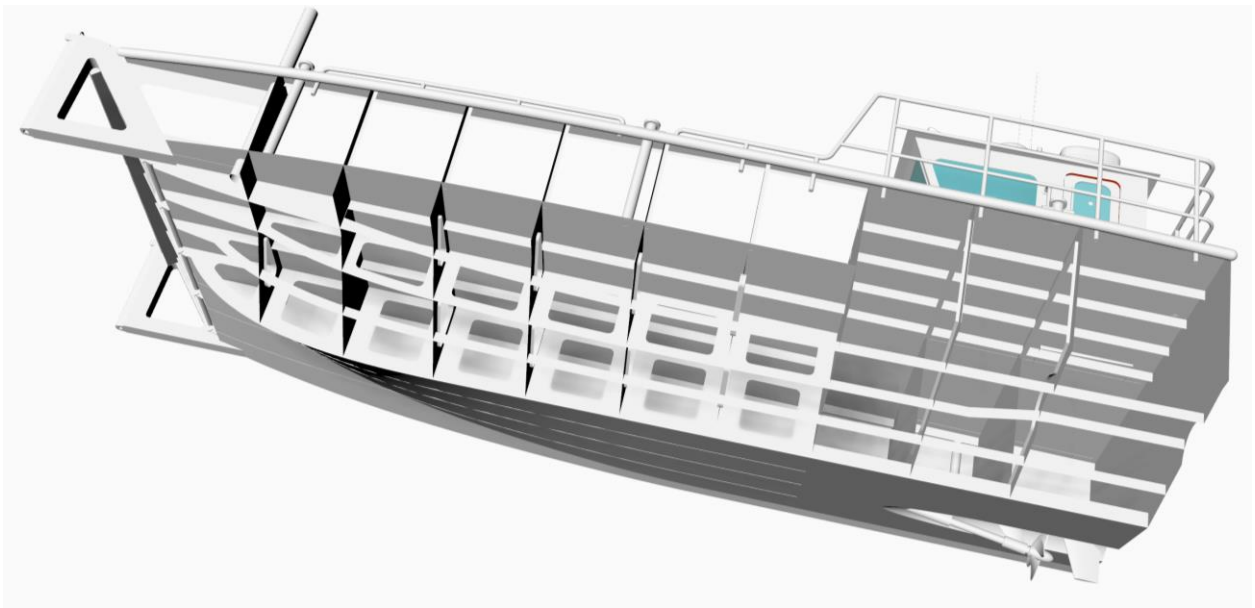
Розрахунок маси корпусних конструкцій судна-платформи
